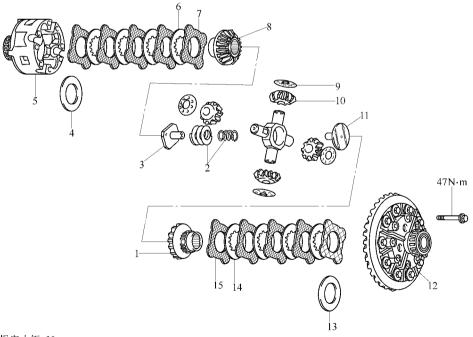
4 小齿轮型式零件分解图 1—RH 壳 2—小齿轮 3—小齿轮止推垫圈 4—LH 壳 5—侧齿轮止推垫圈 6—侧齿轮 7—十字轴
